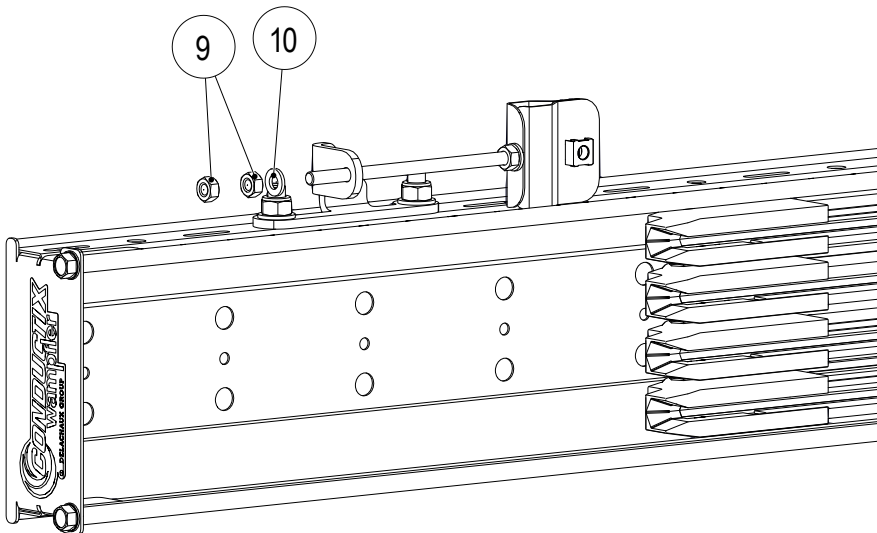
Gewindestange mit den Verschraubungen (9 und 10) kontern
